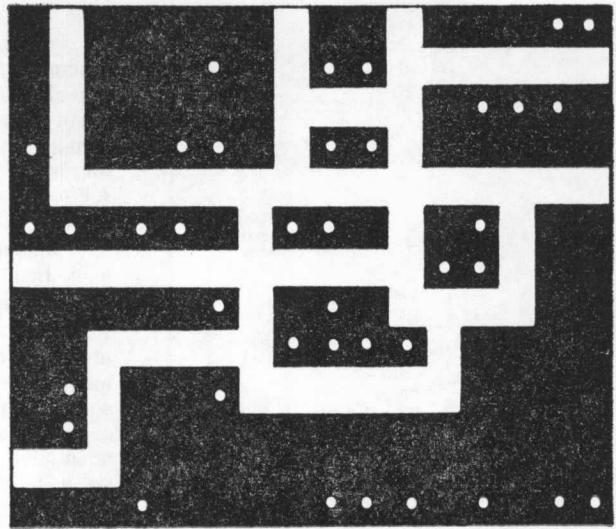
Sugestão para a plaqueta de circuito impresso a ser utilizada.
